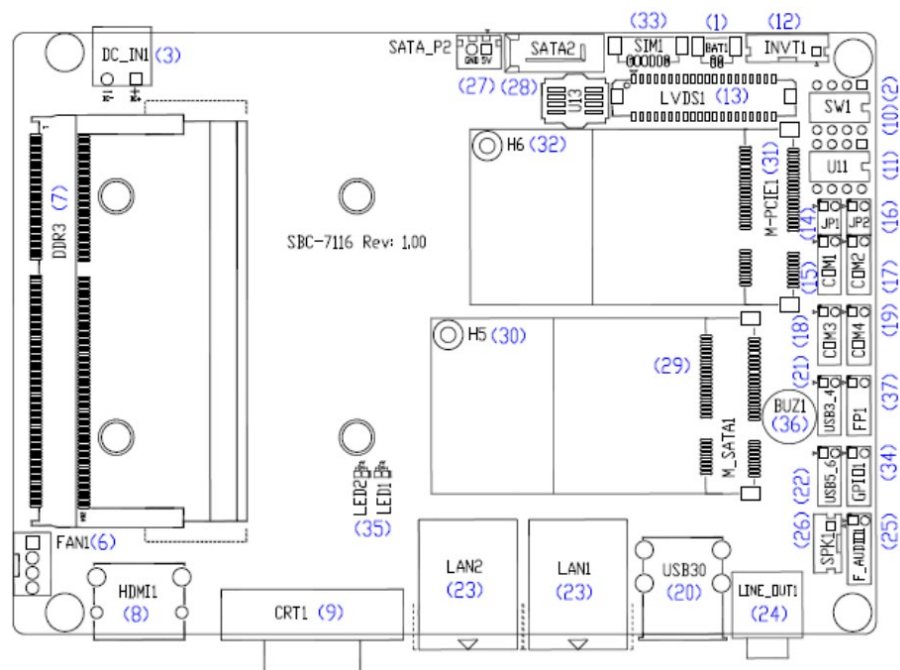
SBC-7116 - Anschlüsse und Jumper - Draufsicht
